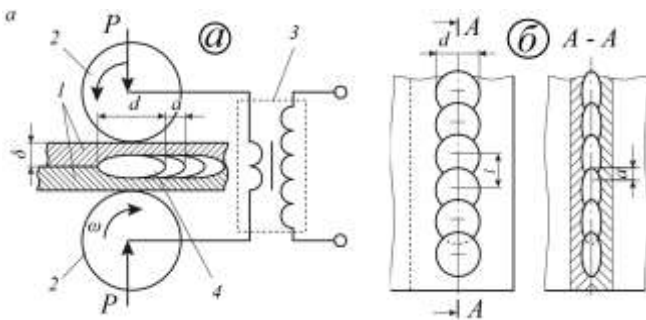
Схема процесу шовного зварювання (а) і шовного зварного з'єднання (б)
